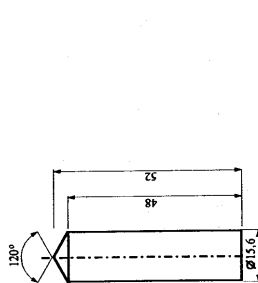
Pistón cilíndrico de bronce, dimensiones en mm.
